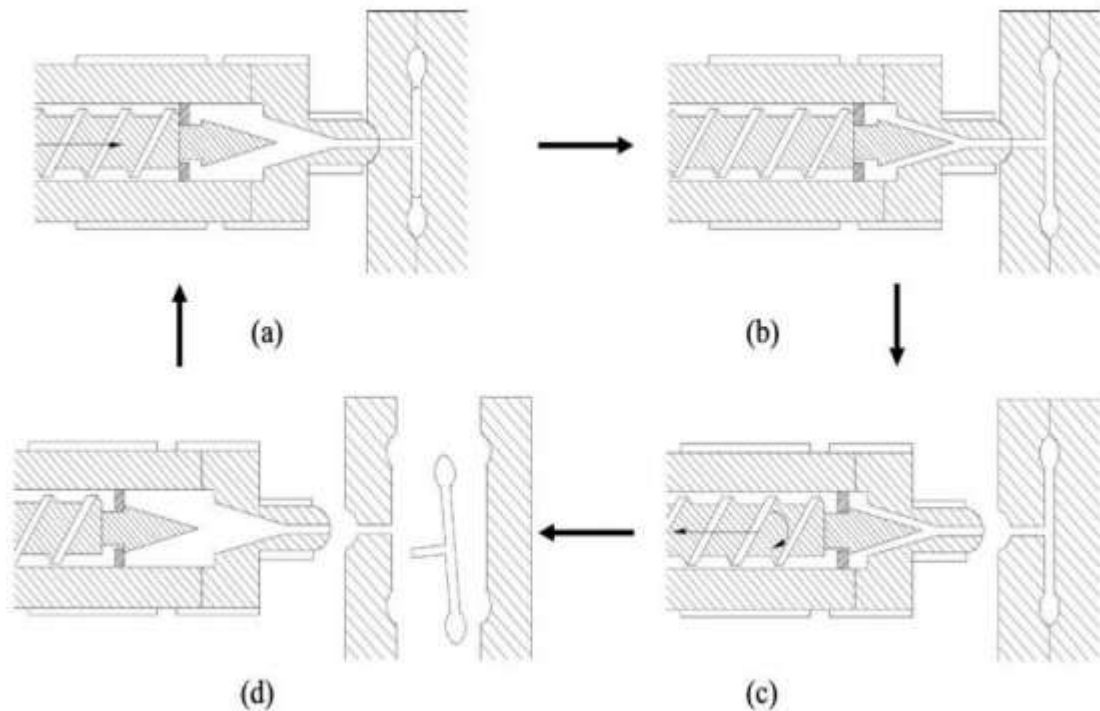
Ciclo de injeção. a) Fechado de molde; b) enchimento; c) compactação; d) abertura do molde e extração
